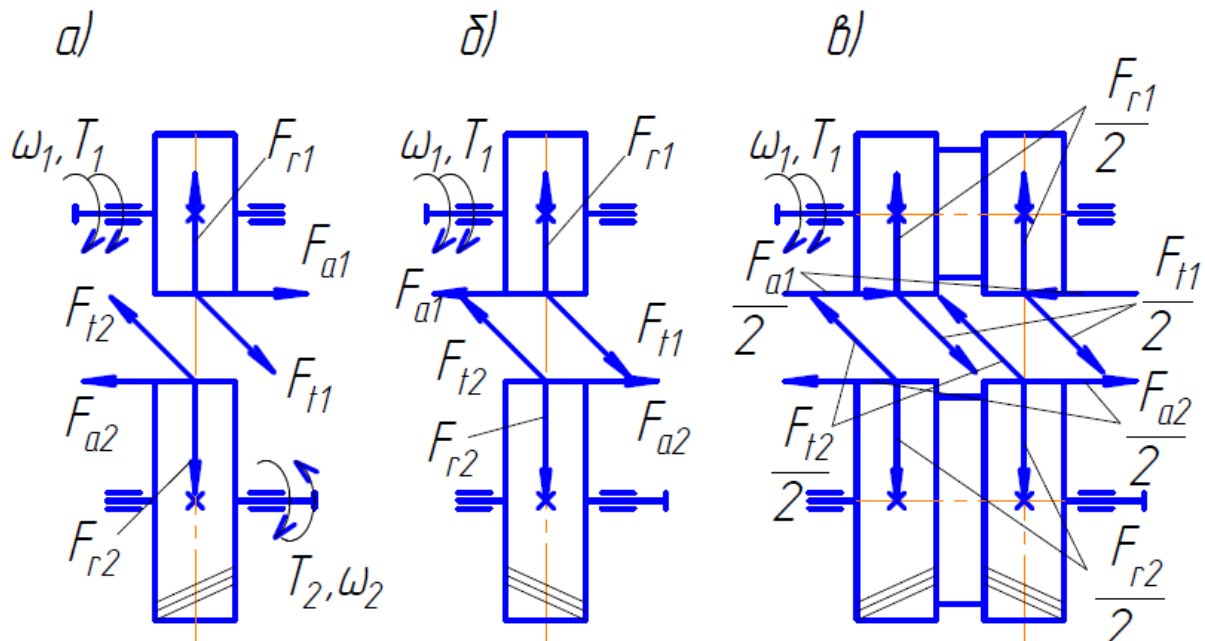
Схема сил в зачепленні циліндричної передачі:
